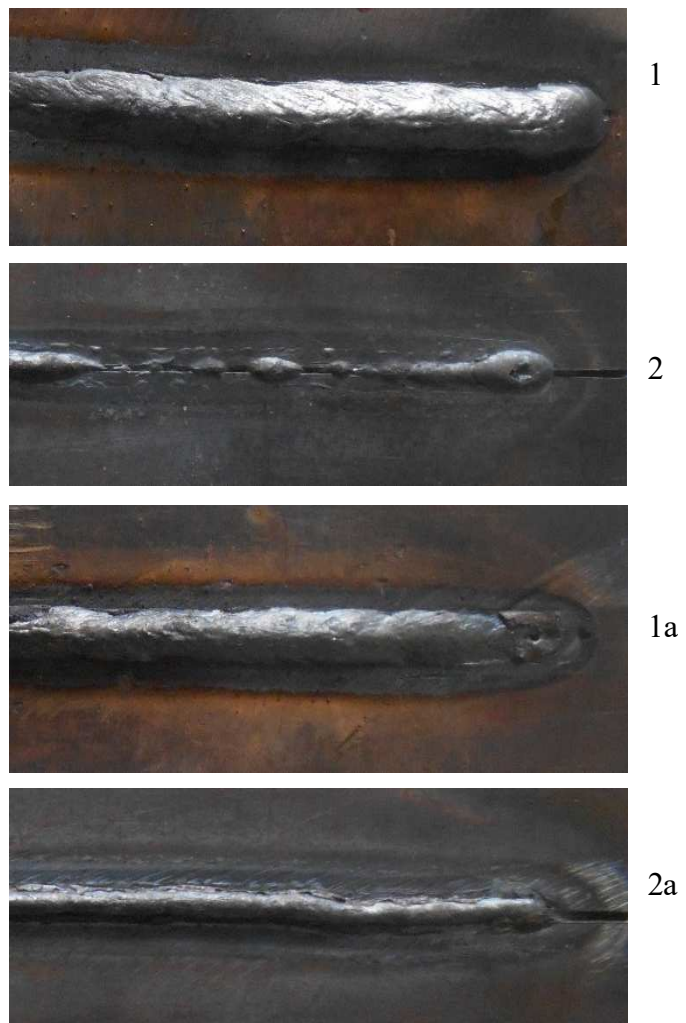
Фрагменти стикового зварювання пластин в нижньому положенні: 1, 2 – зварювання з конвенційною подачею дроту, зовнішній вигляд і зворотна сторона відповідно; 1а, 2а – зварювання з дозованою подачею дроту, зовнішній вигляд і зворотна сторона відповідно
